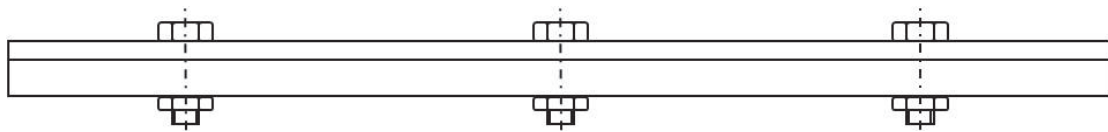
montage composé d'une poutre « fine » avec une poutre « massive » assemblées longitudinalement pas x boulons uniformément répartis sur la longueur d'assemblage
